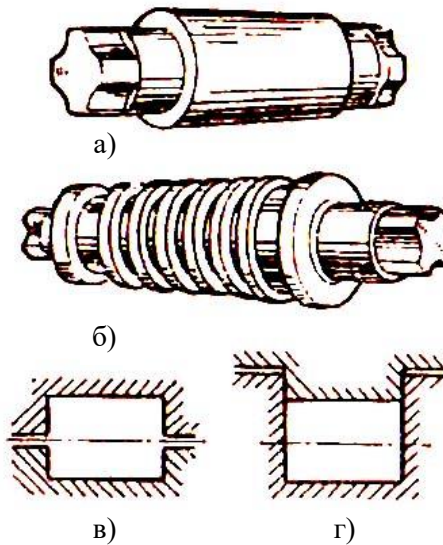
Прокатные валки и калибры: а – валок гладкий; б- валок ручьевой; в – калибр открытый; г – калибр закрытый
